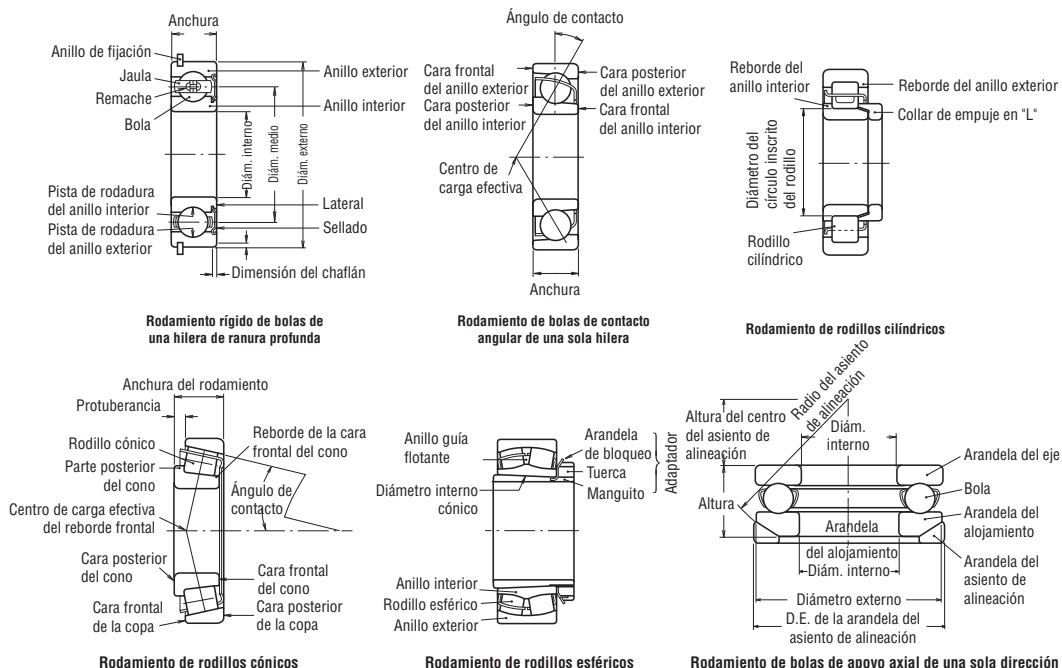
Nomenclatura para las partes de los rodamientos
